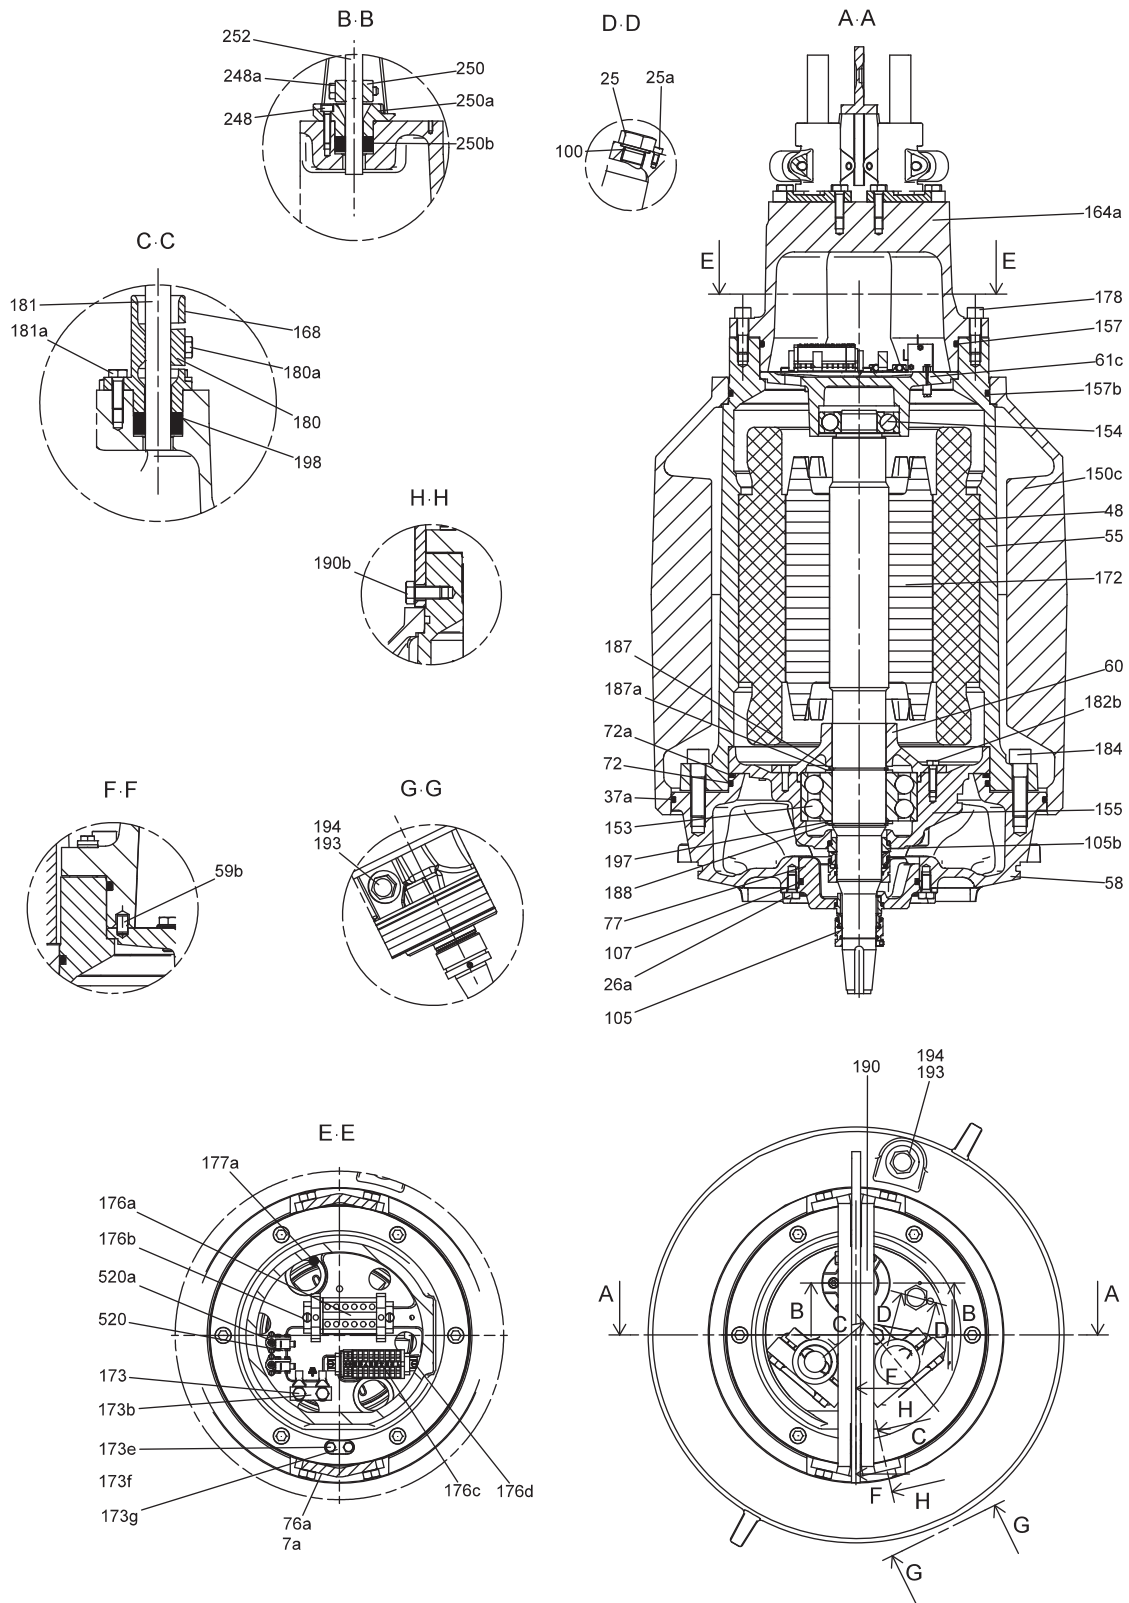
Взрывозащищённый двигатель без охлаждающего кожуха
